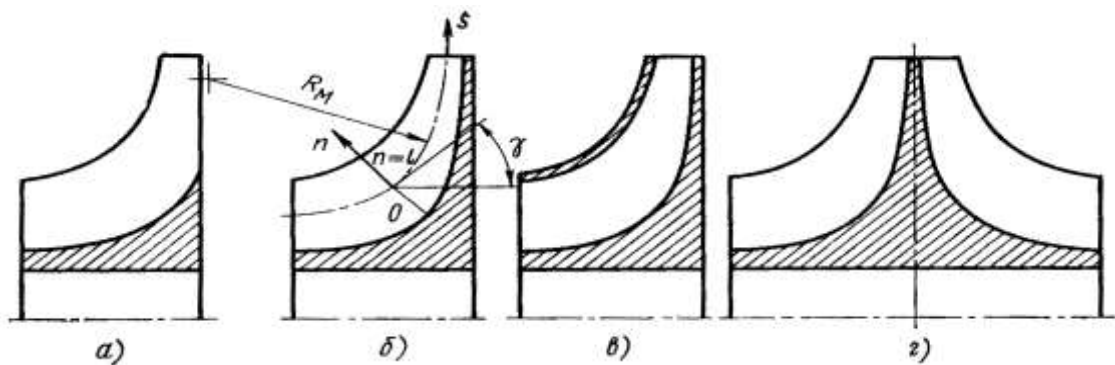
Типи конструктивного виконання робочих коліс компресора.
